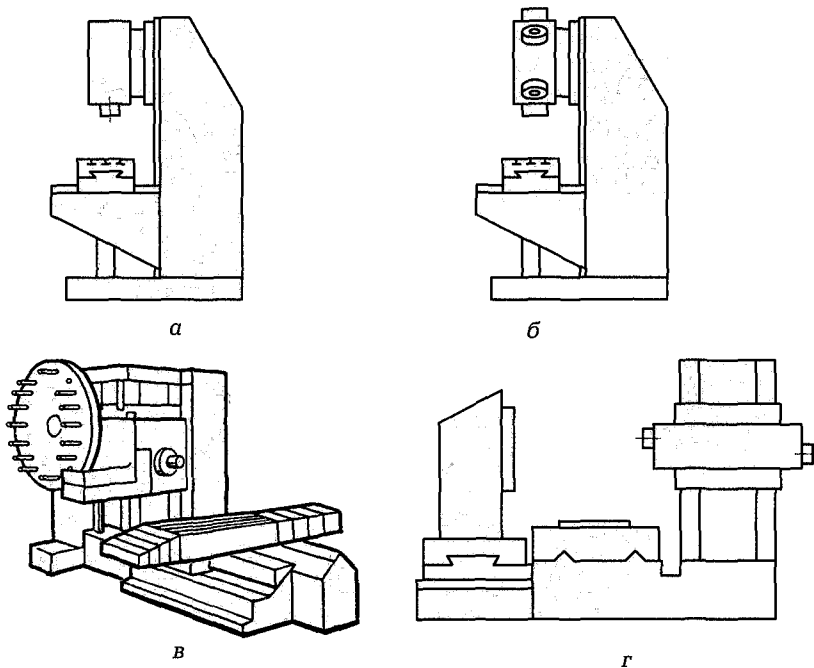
Фрезерные станки с числовым программным управлением:
